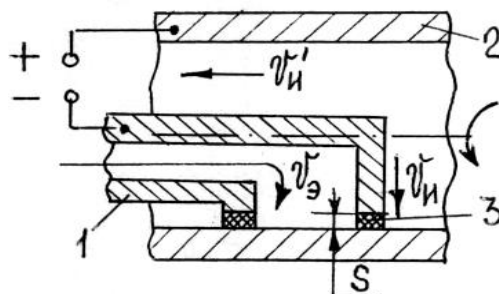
Схема точіння внутрішніх поверхнь: 1 – електрод-інструмент; 2 – заготовка; 3 – прокладки діелектричні
